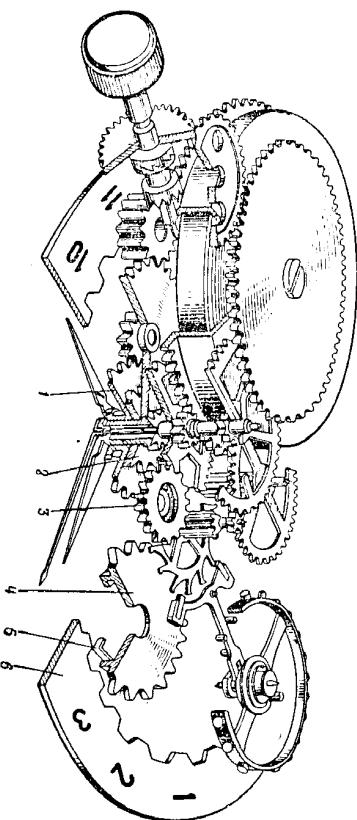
Кинематическая схема календарного устройства часов «Полёт» 2414:
